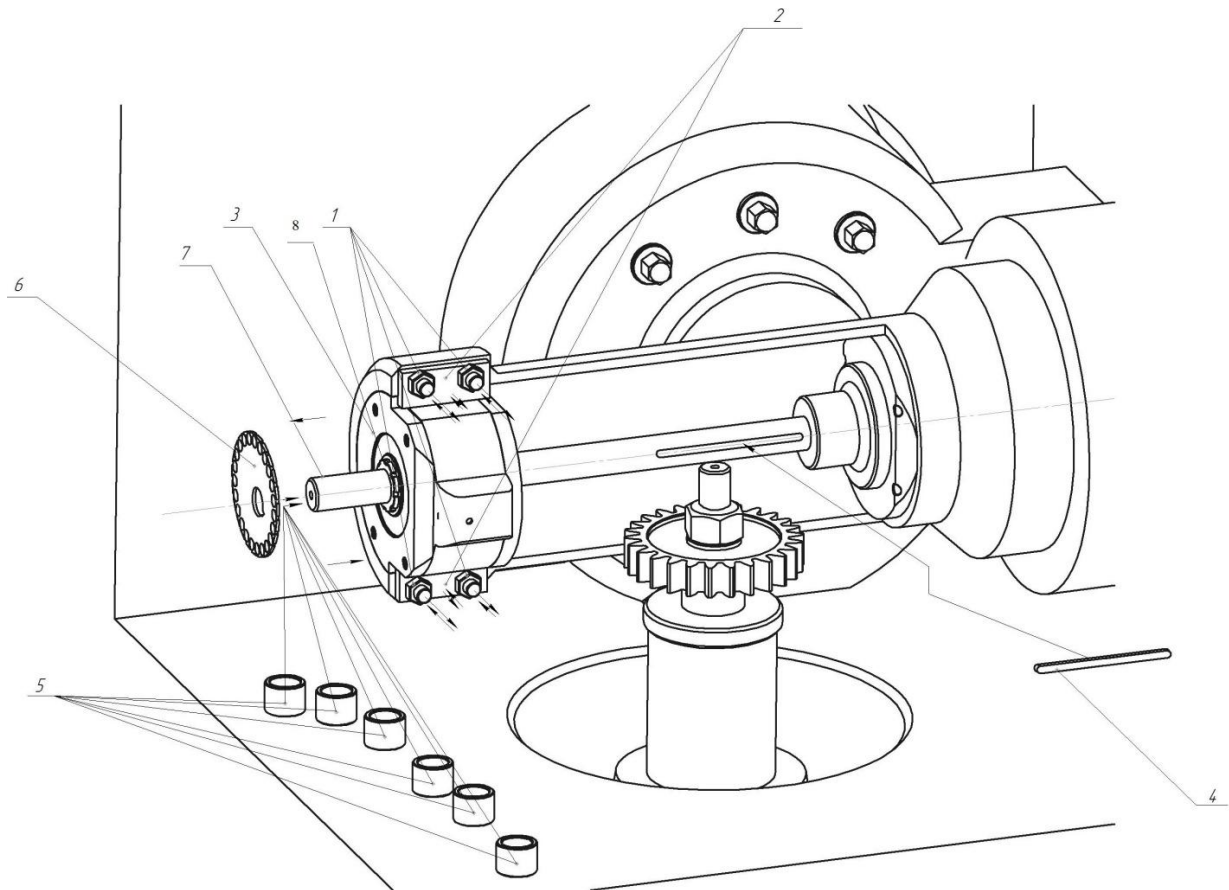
Встановлення дискового інструмента на зубофрезерний верстат мод.5А312
